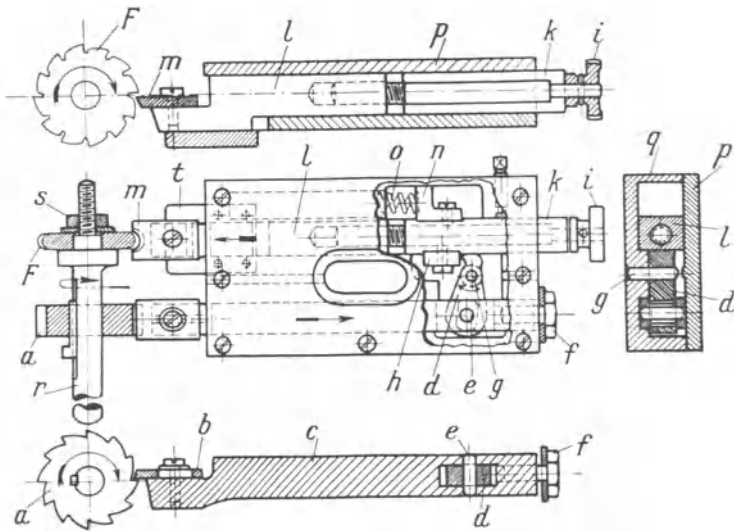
Fräser-Hinterdrehvorrichtung für Drehbänke.
